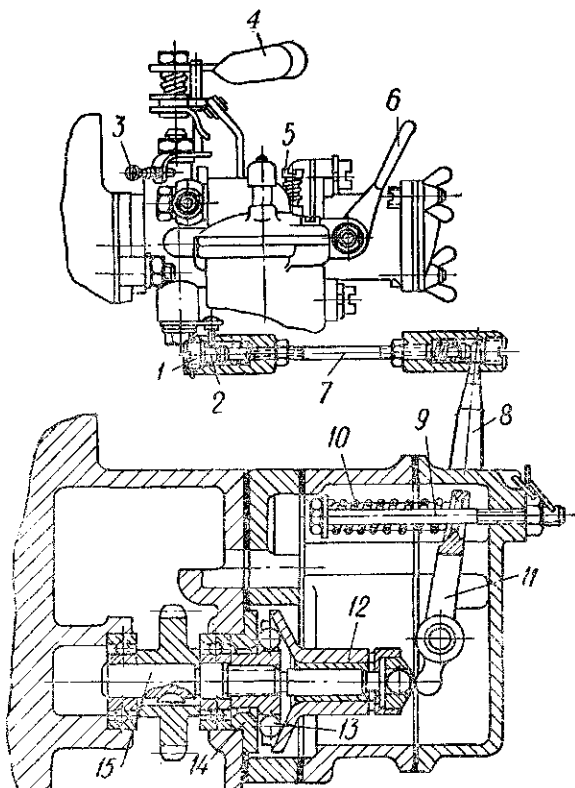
Регулятор пускового двигателя и органы управления карбюратором:
